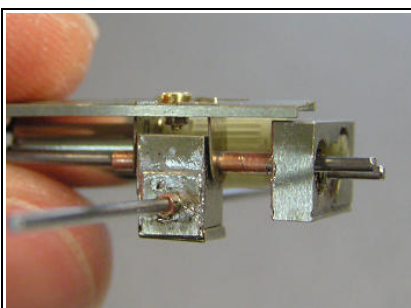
Das Vorgelegegetriebe bis zum Anschlag aufstecken.
